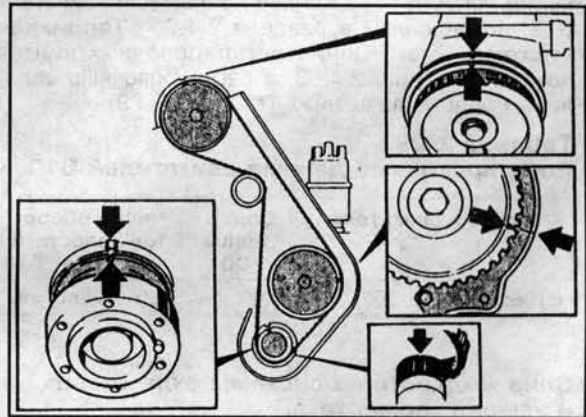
Установка зубчатого ремня привода механизма газораспределения
